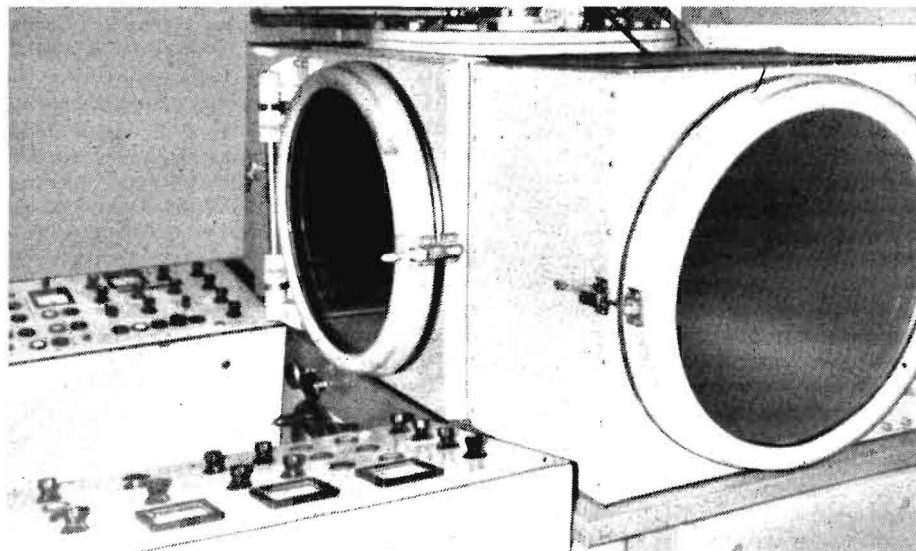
Schweißvorrichtung zum Elektronenstrahlschweißen von gleichzeitig 6 Getrieberädern unter Schräglage
